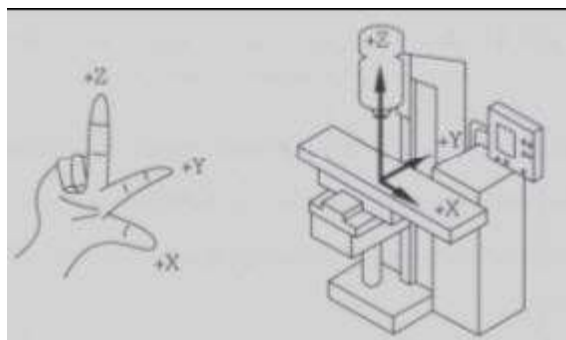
CNC Machining Center ที่ใช้ในปัจจุบัน
